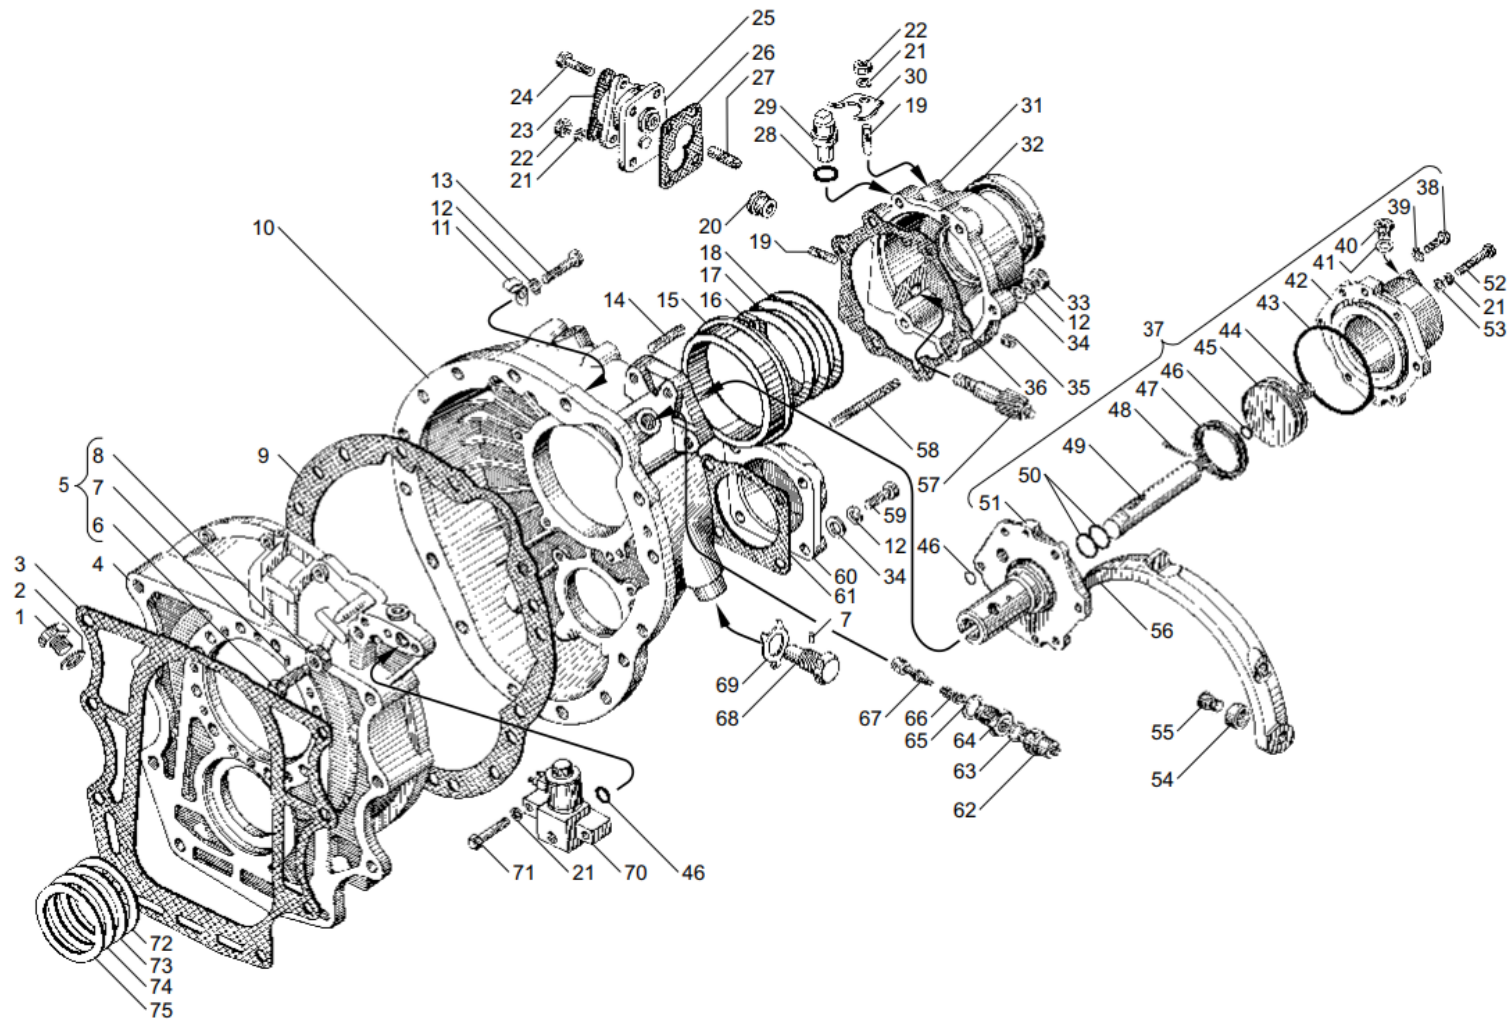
КАРТЕР ДЕМУЛЬТИПЛИКАТОРА КОРОБКИ ПЕРЕДАЧ (алюминиевый)
